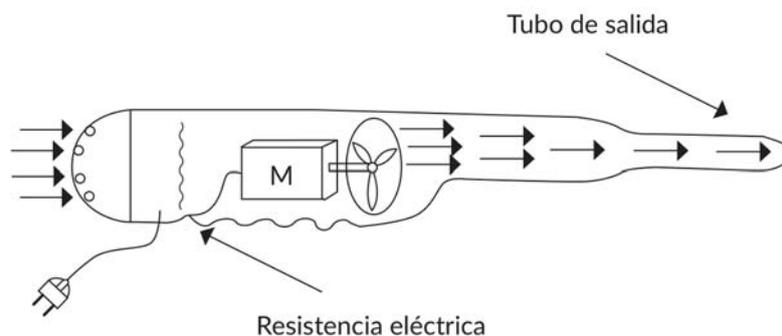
Soldador térmico de PVC. Fuente: Elaboración propia.
